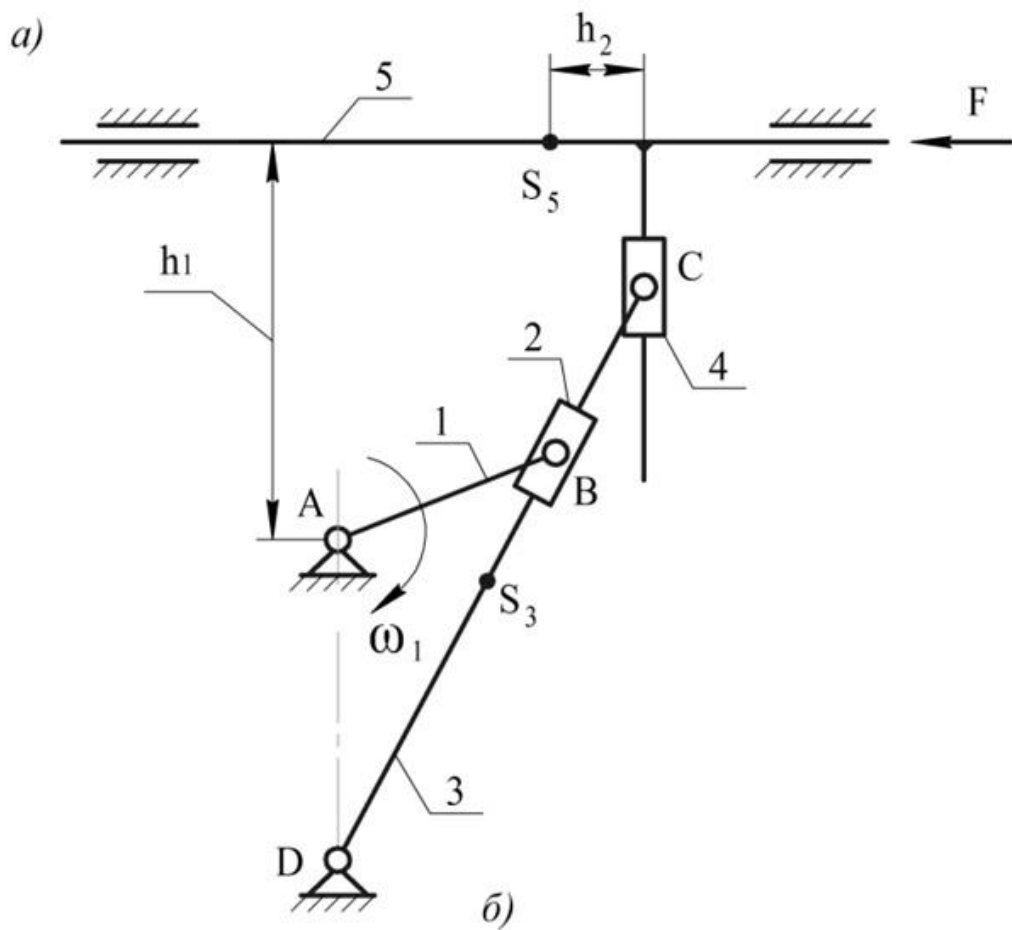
Схема рычажного механизма поперечно-строгального станка с качающейся кулисой
